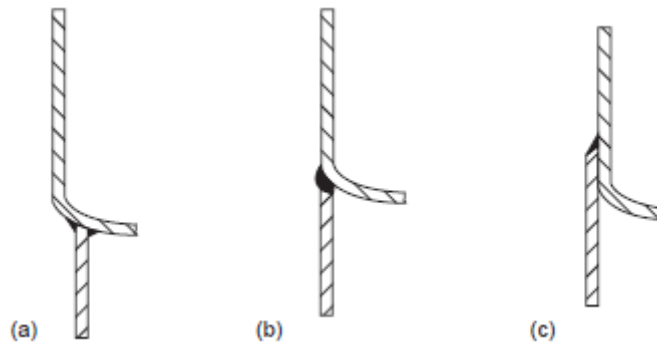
(a) Soldadura en la parte inferior. (b) Soldadura a ras del recipiente. (c) Soldadura en el exterior de la carcasa (Sinnott)
